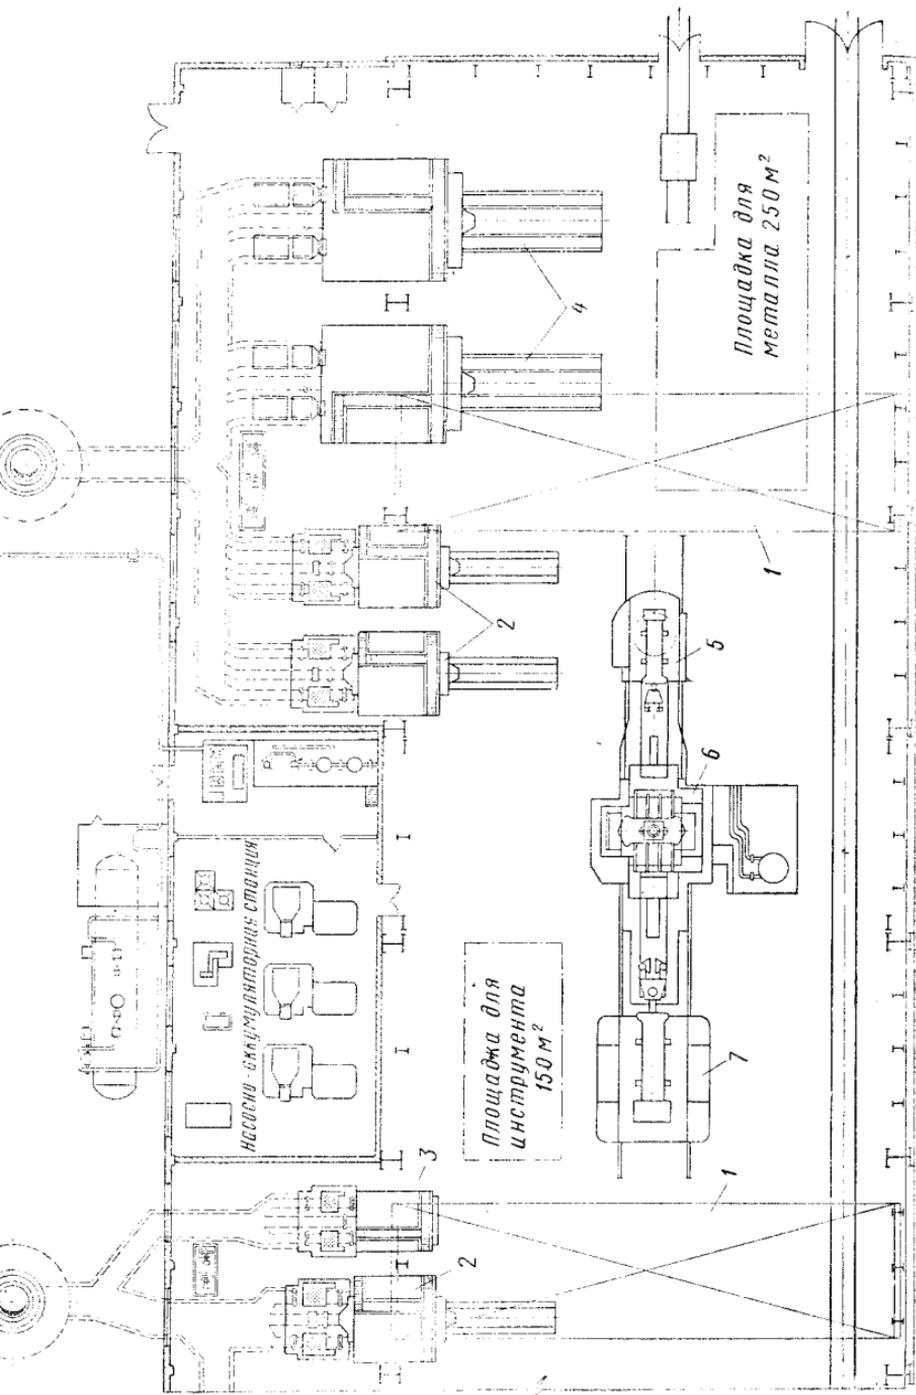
Расположение оборудования на участке гидравлического ковочного пресса:
